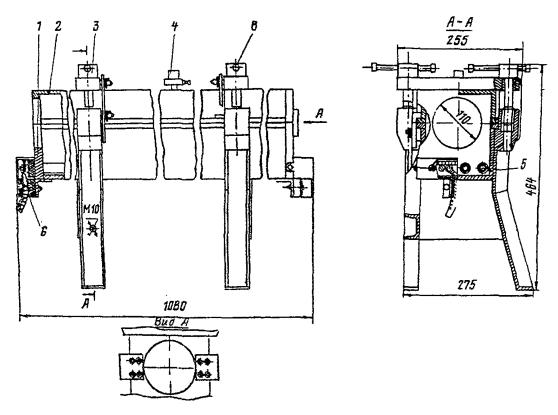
Схема вулканизатора парового АПК иля выполнения концевих заделок: 1 - корпус; 2 - кражи; 3 - пракичее устройство; 4 - клапан; 5 - электровегрезатель; 6 - стопоряюе устройство
